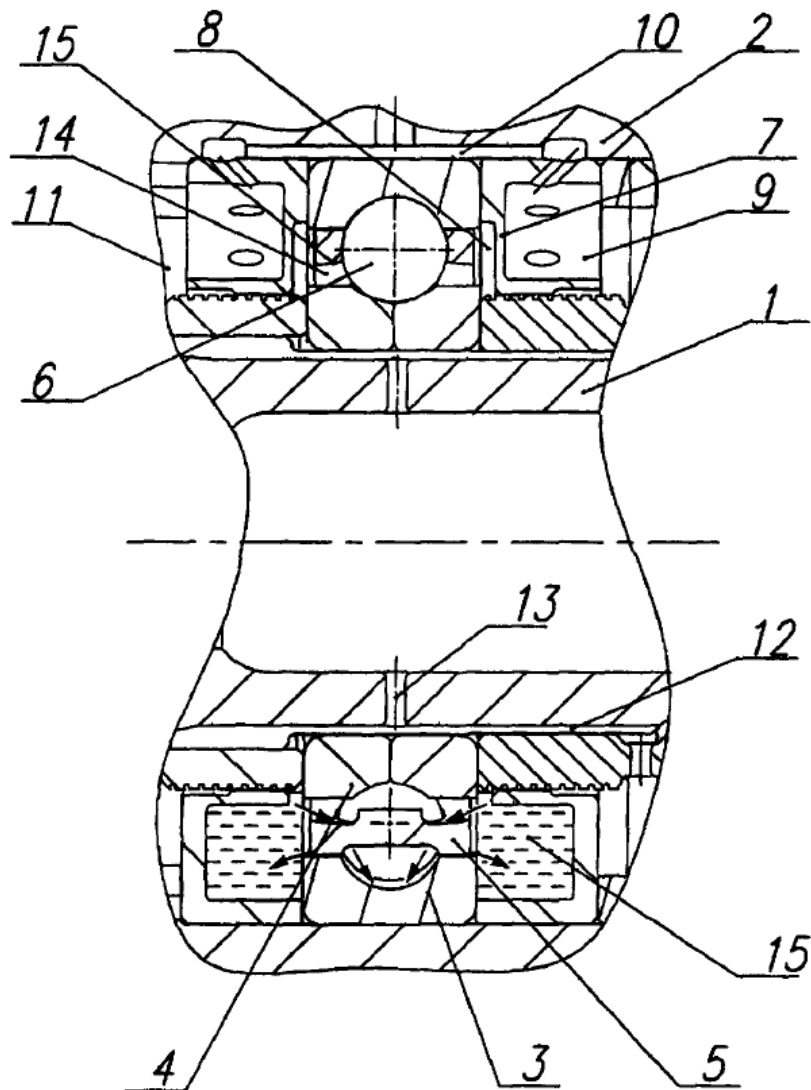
Опора с подшипником, смазываемым консистентной смазкой
